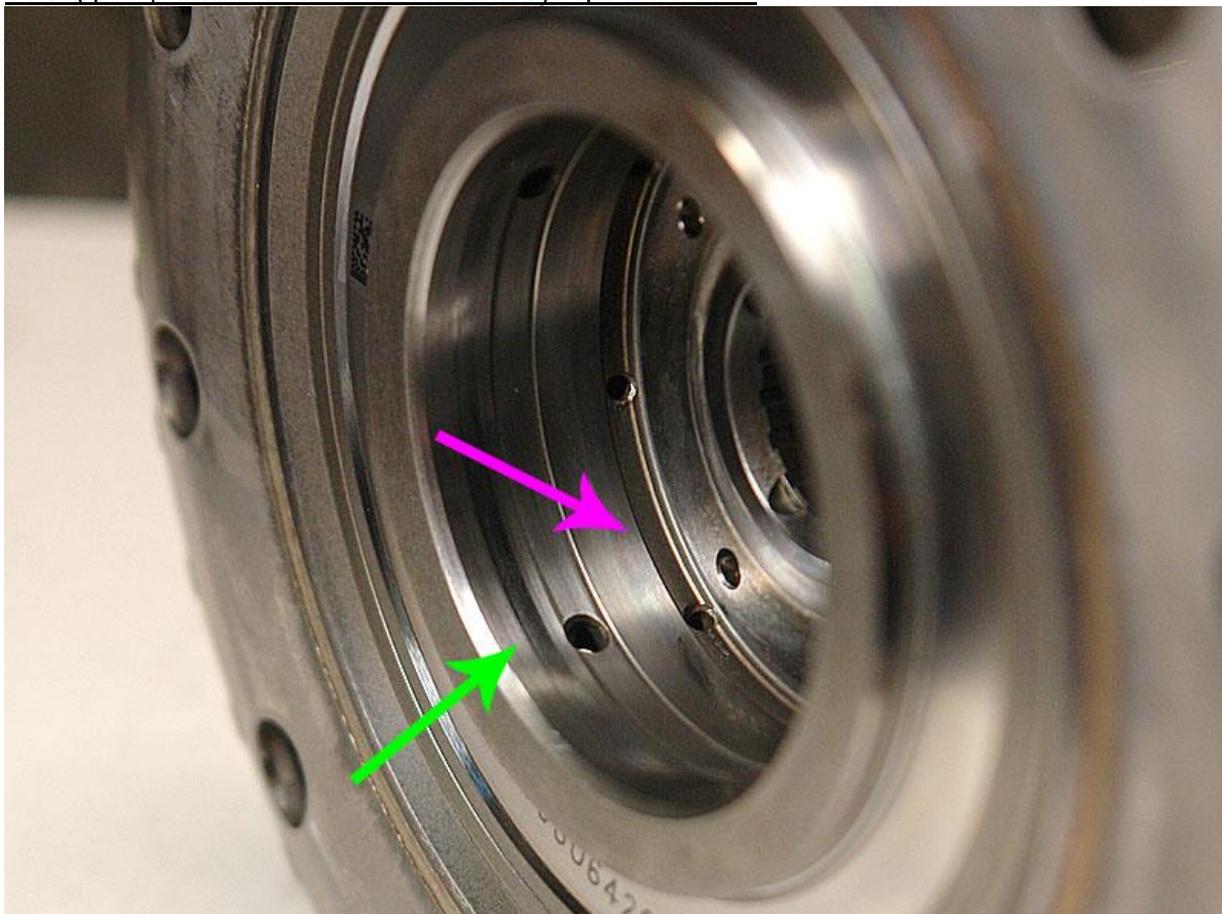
Поверхность работы вращающихся уплотнительных колец на корпусе сцепления OD (стрелками обозначены следы работы колец: зеленой – четкий след, розовой – нечеткий).
